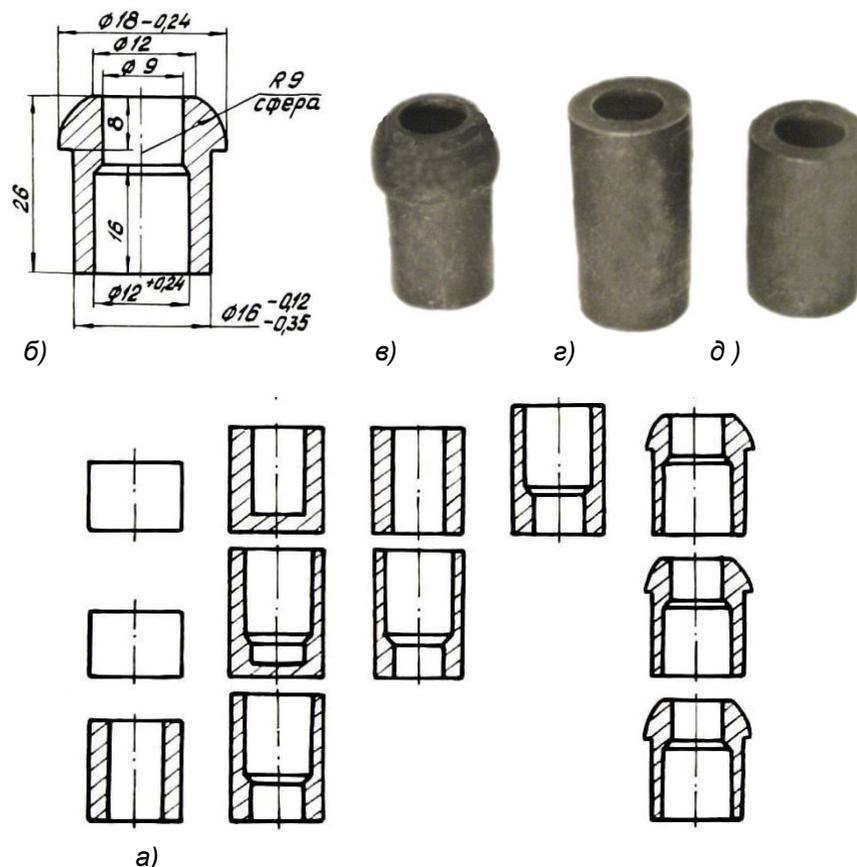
Возможные варианты (а) процессов холодной объемной штамповки детали «ниппель» (б, в); полуфабрикат (г) и исходная трубная заготовка (д)
